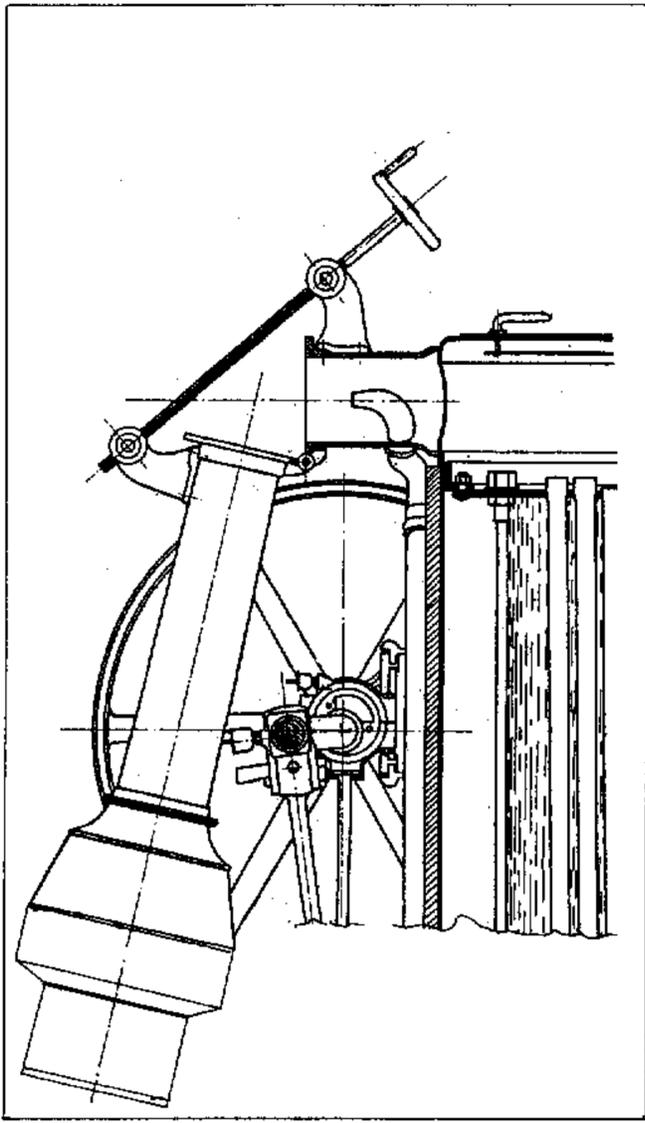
/5: Einrichtungen zum Ablegen und Aufrichten des Kamins mit Verstellspindel (Maschinenfabrik von Th. Flöther, um 1900)
